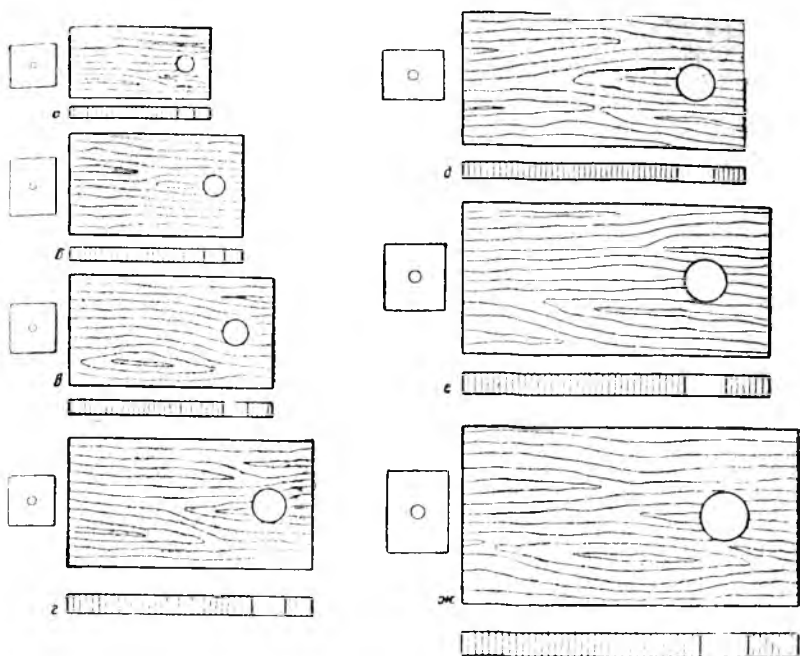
Размеры и формы крышек и донышек в звуковых приборах:
